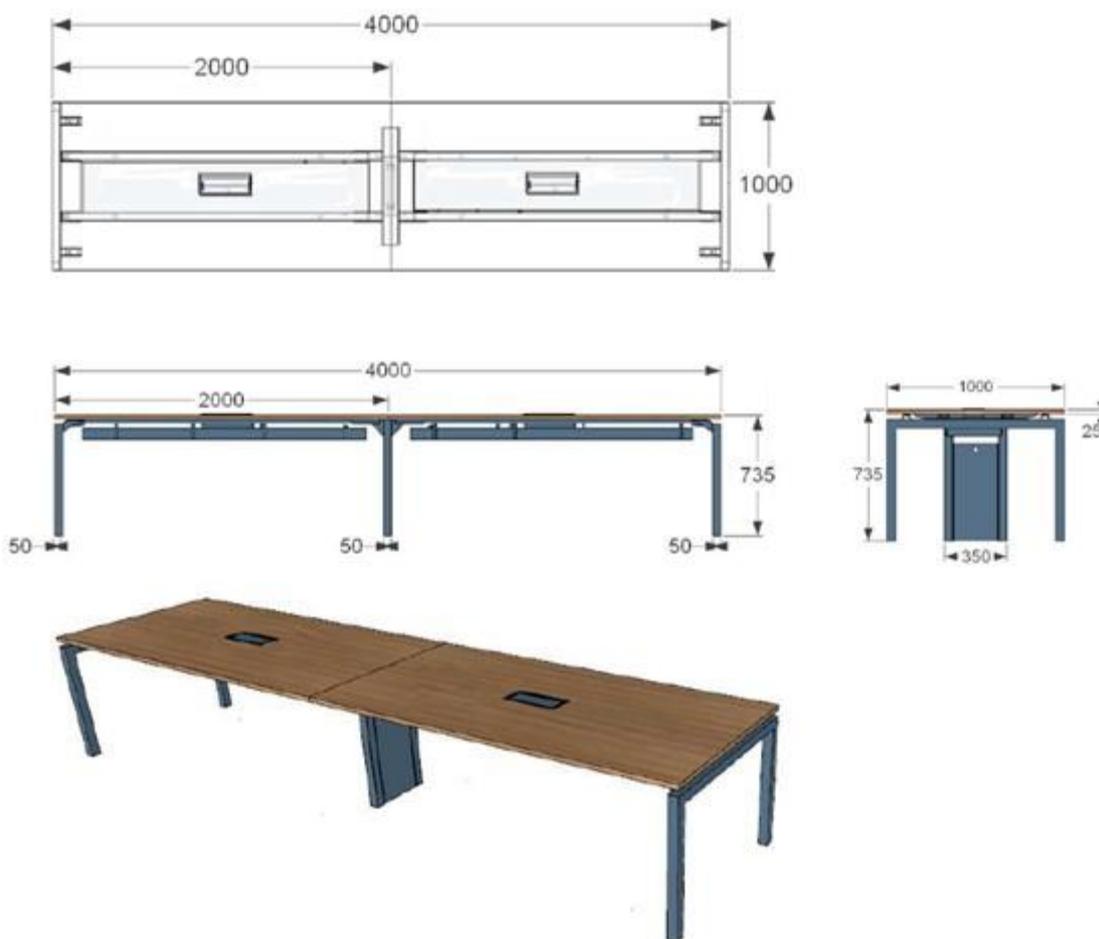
Planta baixa, vista frontal, vista lateral e perspectiva modelo item 23
